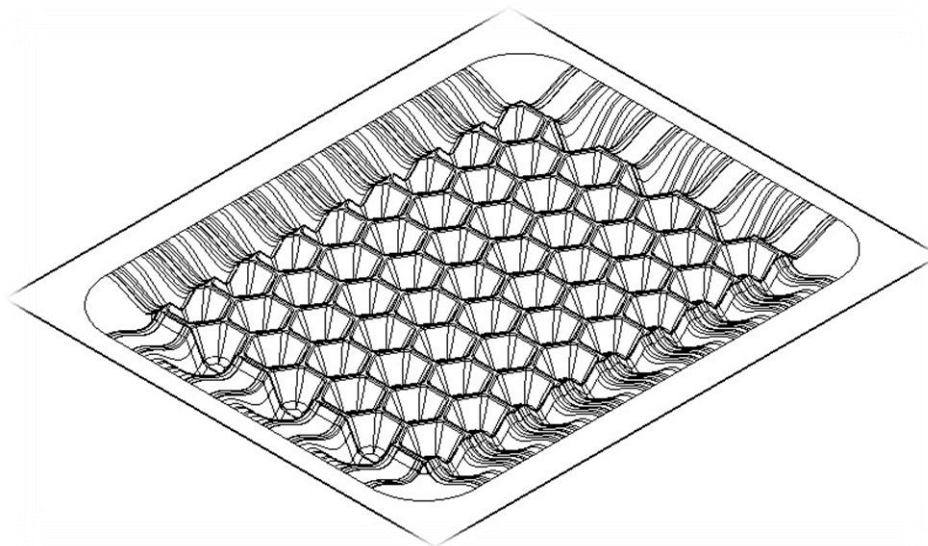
Подготовка модели оснастки для изготовления заполнителя из ПКМ с изолированными дискретными элементами, расположенными в шахматном порядке
